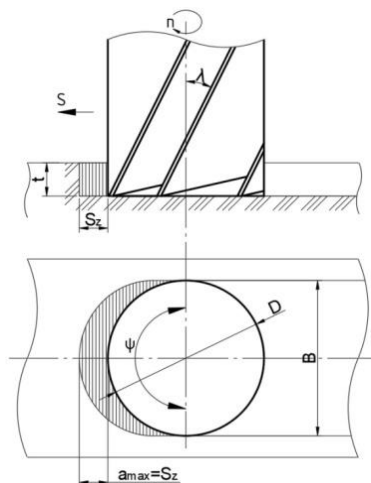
Схема фрезерования: D - диаметр ФРО; B – ширина фрезерования;
